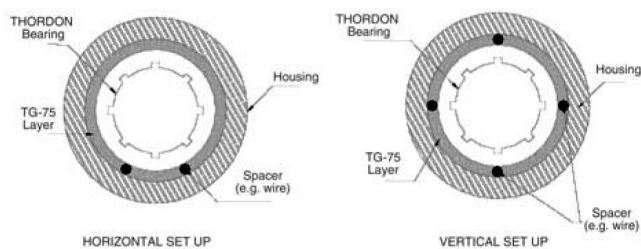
Alambre utilizado para mantener el cojinete excéntrico en la carcasa (el dibujo no está a escala)
